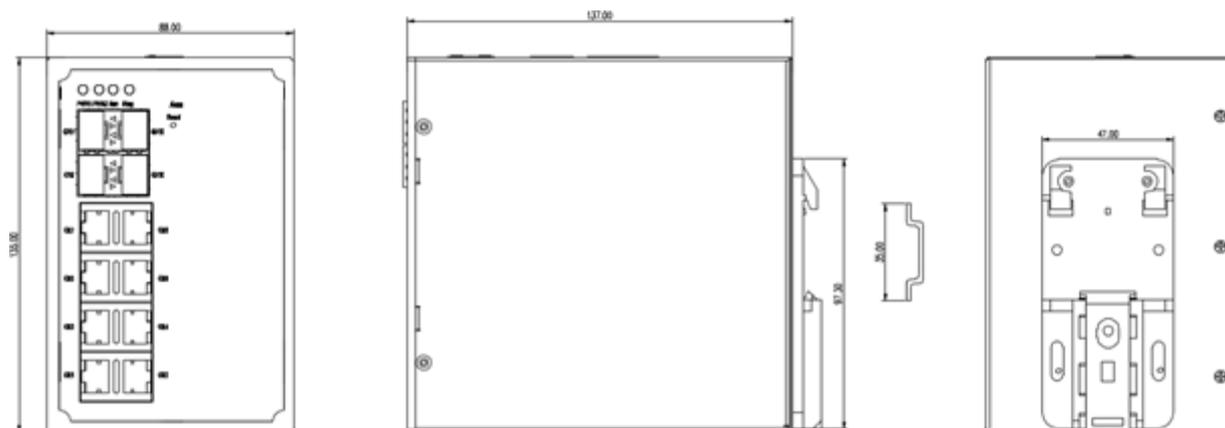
Габаритный чертеж корпуса «Тип 2» с креплением на DIN-рейку
